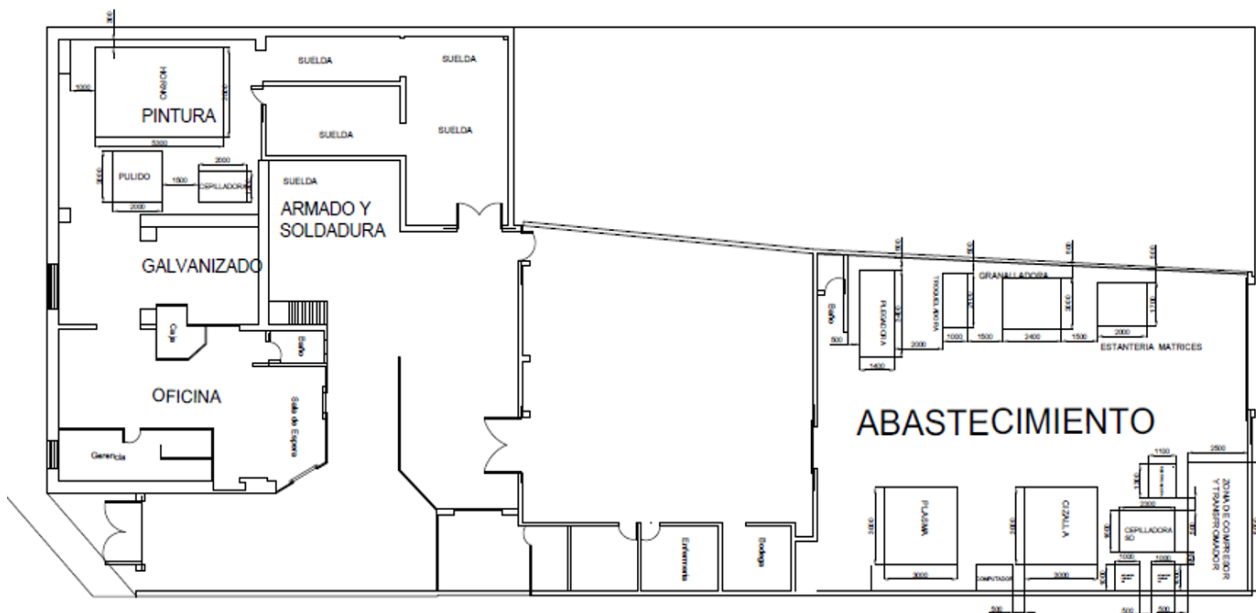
Distribución de las áreas de trabajo en la empresa metalmecánica.
